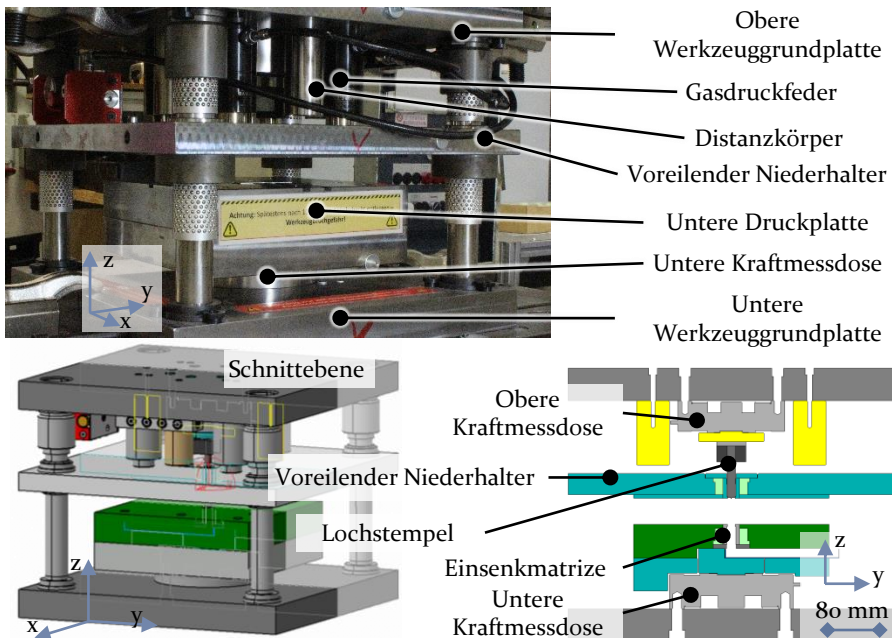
Werkzeug zum Einsenken und Lochen des Aluminium-Trägerblechs
